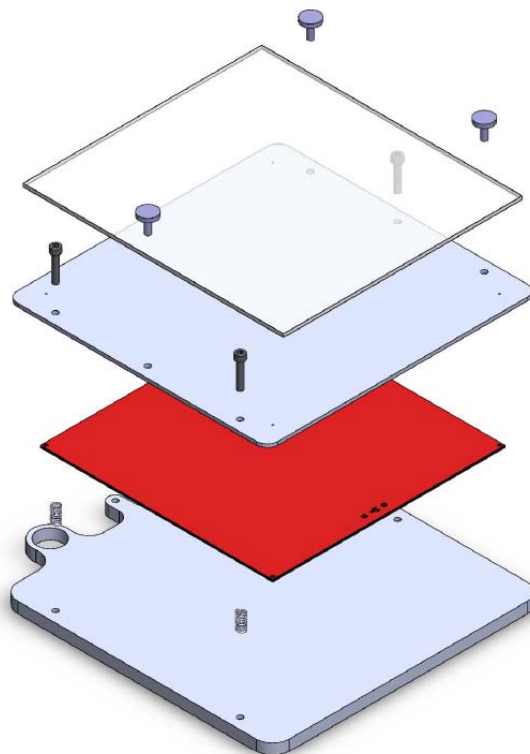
55. Vista explosionada de la plataforma de extrusión
